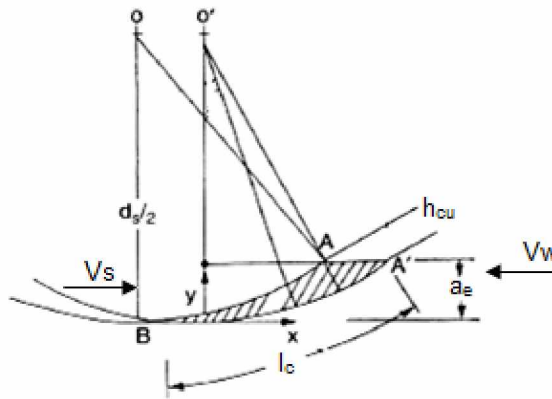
Geometria do cavaco não deformado para o processo de retificação plana tangencial (Adaptado de MALKIN; GUO, 2008).
